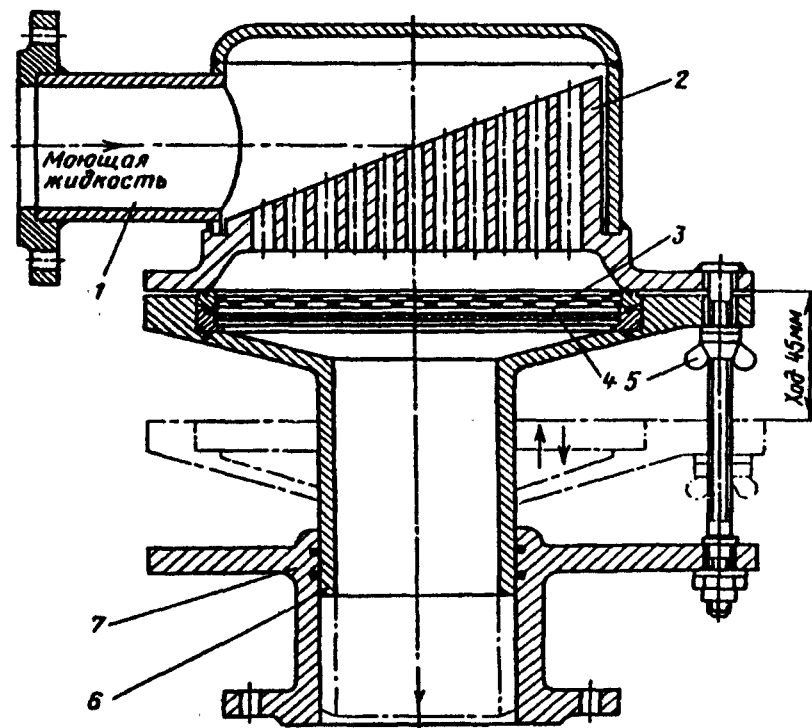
Быстроразъемный контрольный фильтр:
